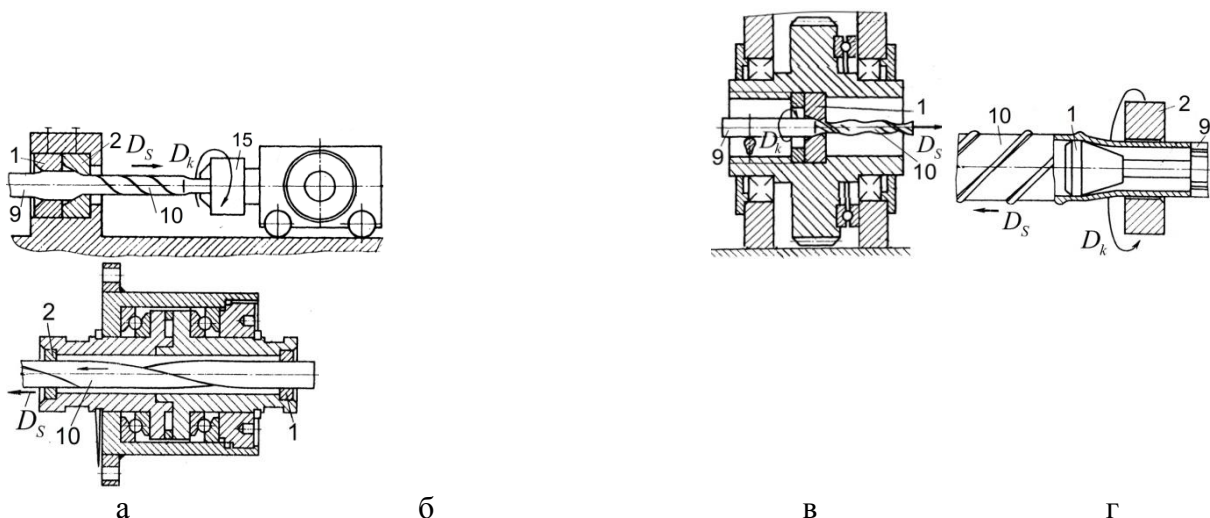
Типові технологічні способи формоутворення ГЗ і ШЗ: 1, 2 - інструменти (волокна, голка, оправа); 9 – початкова заготовка, 10 – скручені ГЗ або ШЗ, 15 - захвати
